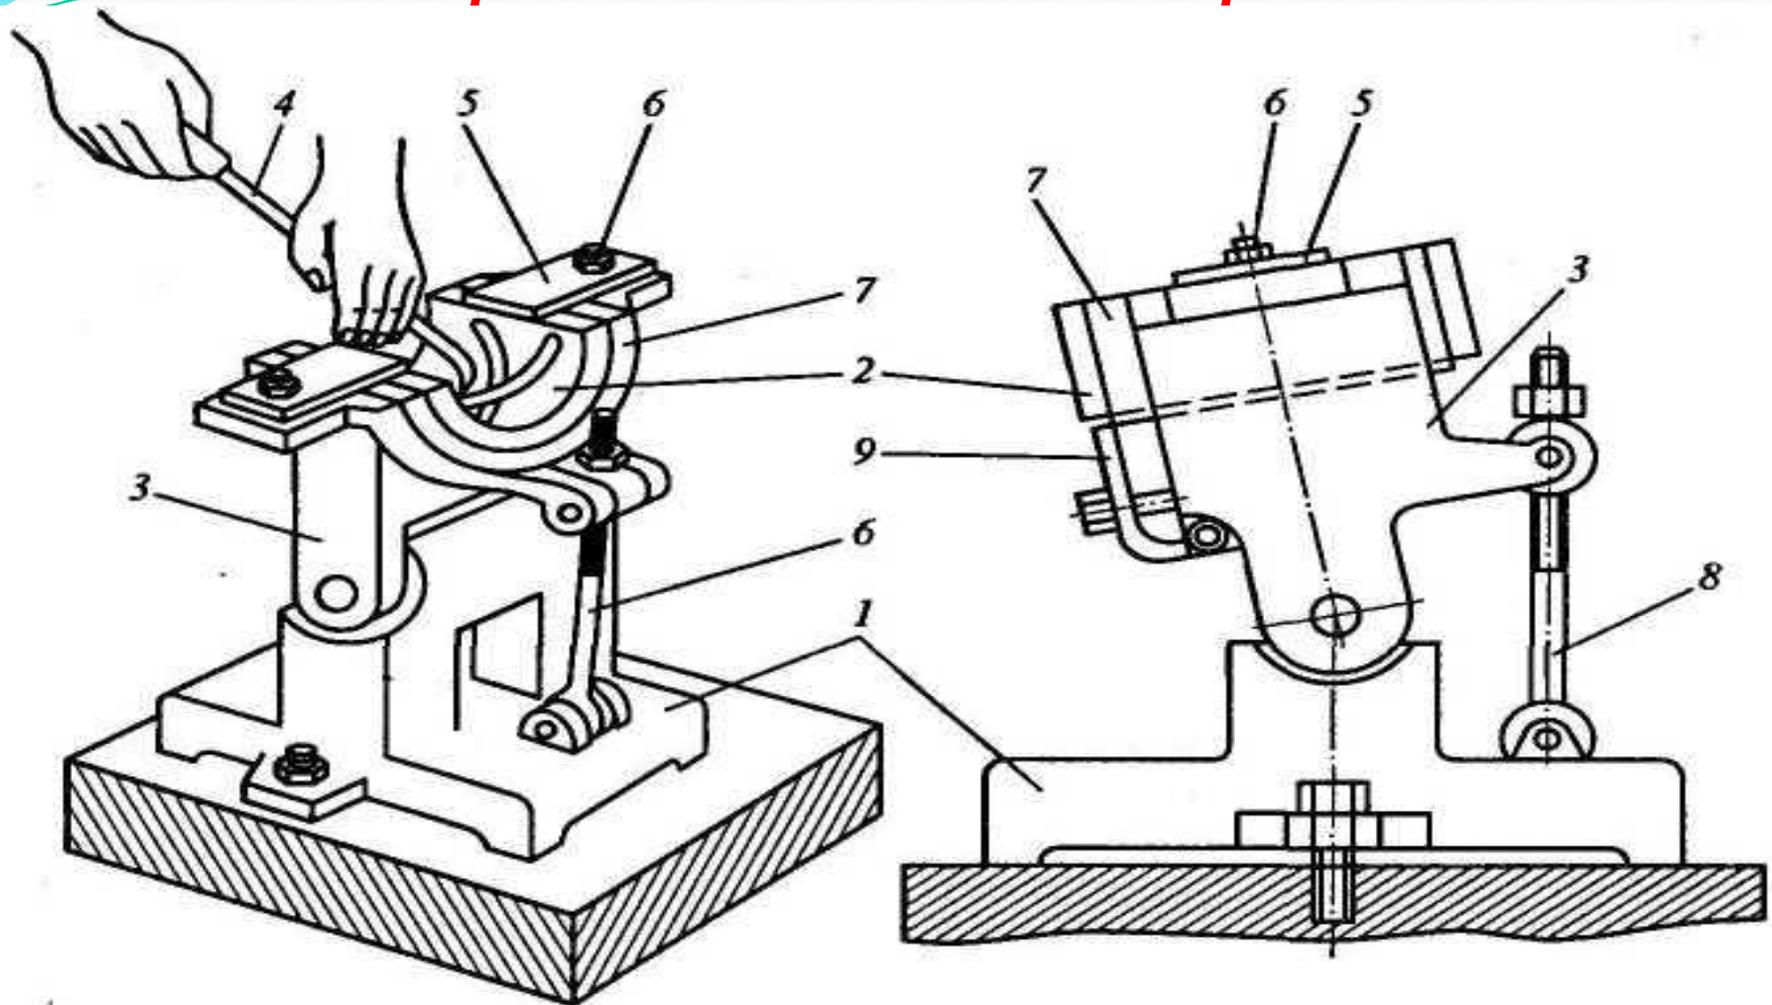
Приспособление для шабрения вкладышей подшипника скольжения: 1 - основание; 2 - вкладыш; 3 - стойка; 4 - шабер; 5 - планка; 6,8- винты; 7 - полукольцо; 9 - прижим
